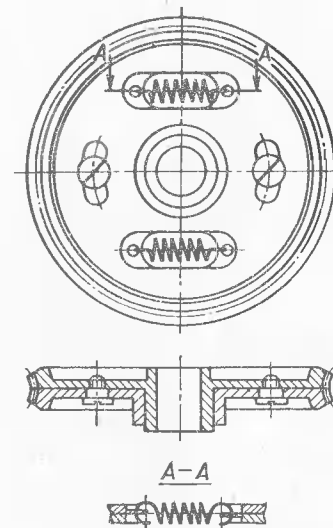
Конструкция зазоровыбирающего червячного колеса с пружиной растяжения
